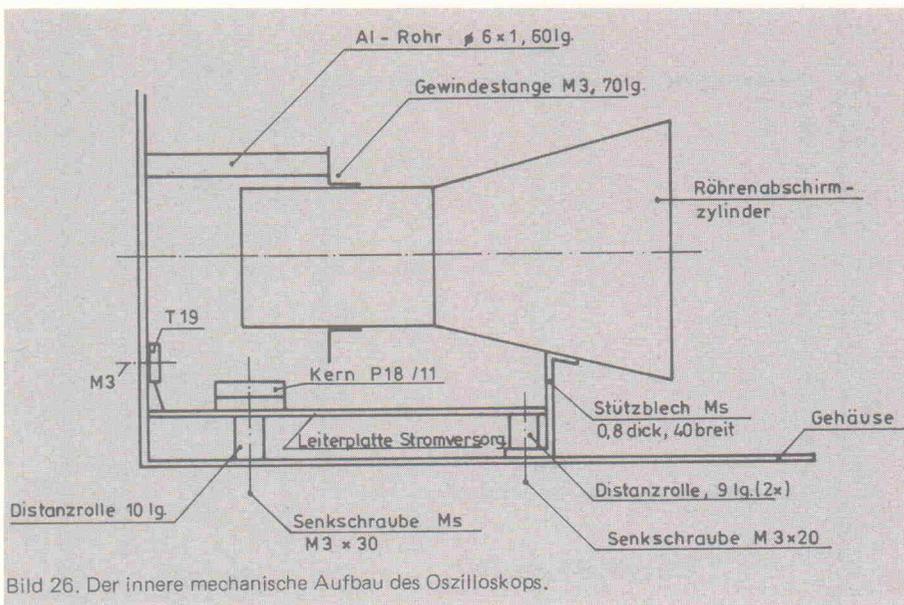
Der innere mechanische Aufbau des Oszilloskops.
